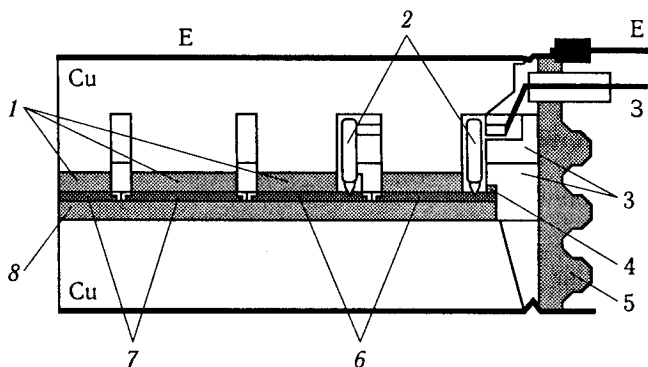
Розріз конструкції IGBT-модуля притискної конструкції: 1 — молібденові прокладки; 2 — зонди; 3 — сепаратори; 4 — рамка; 5 — керамічний корпус; 6 — чіпи IGBT; 7 — чіпи FRD; 8 — молібденовий диск
